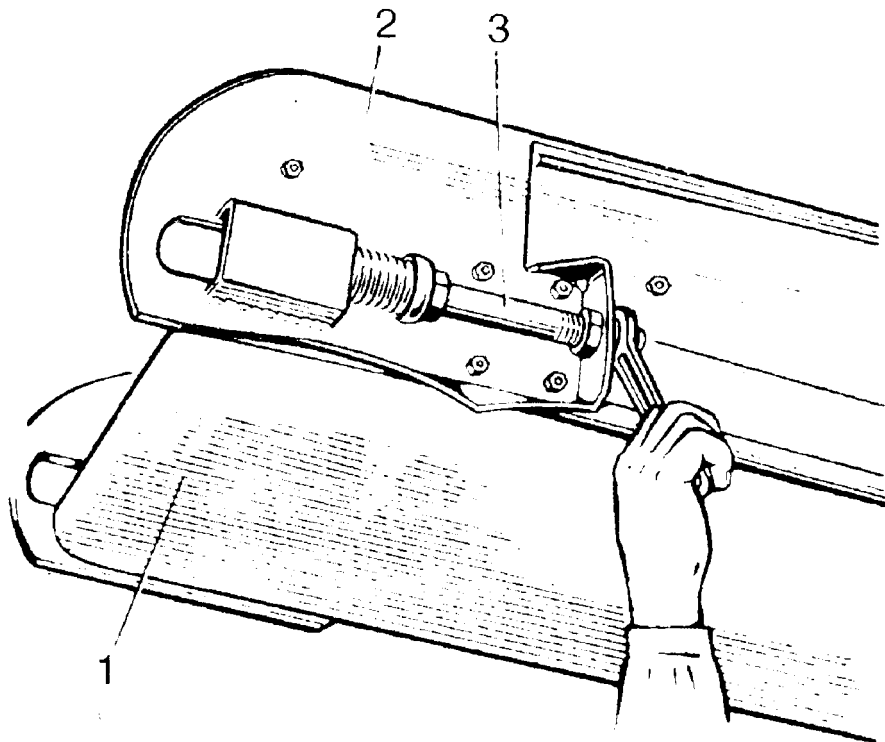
Регулировка натяжения ленты транспортера вороха:
